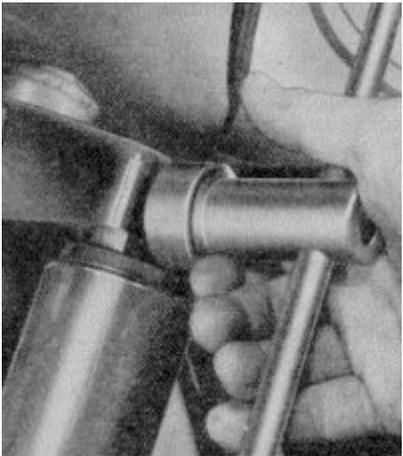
Lösen des Gewindestopfens mit Profilsteckschlüssel 05 MW 24-4
